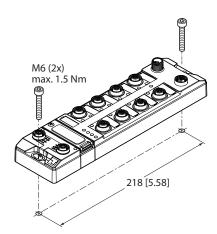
Assemblage de l'appareil sur une plaque de montage
